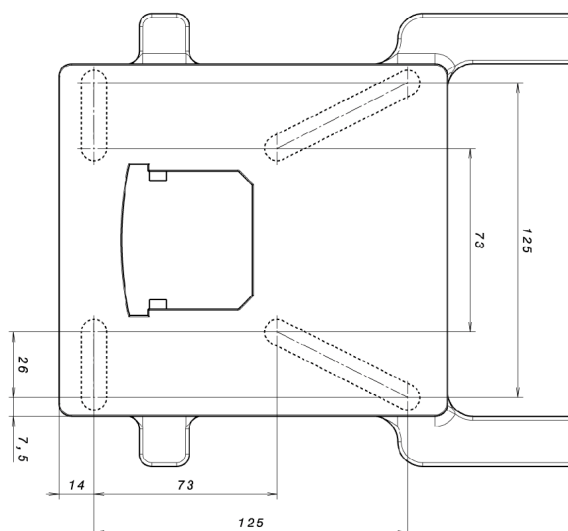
Bohrbild Standard-Adapterplatte BG C
